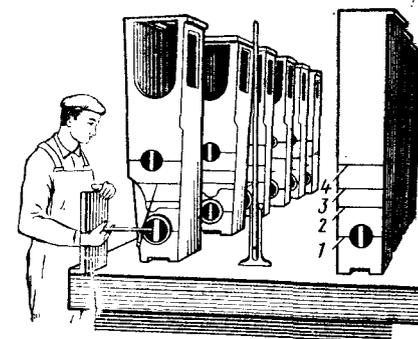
Разметка партии корпусных деталей одним рейсмусом
